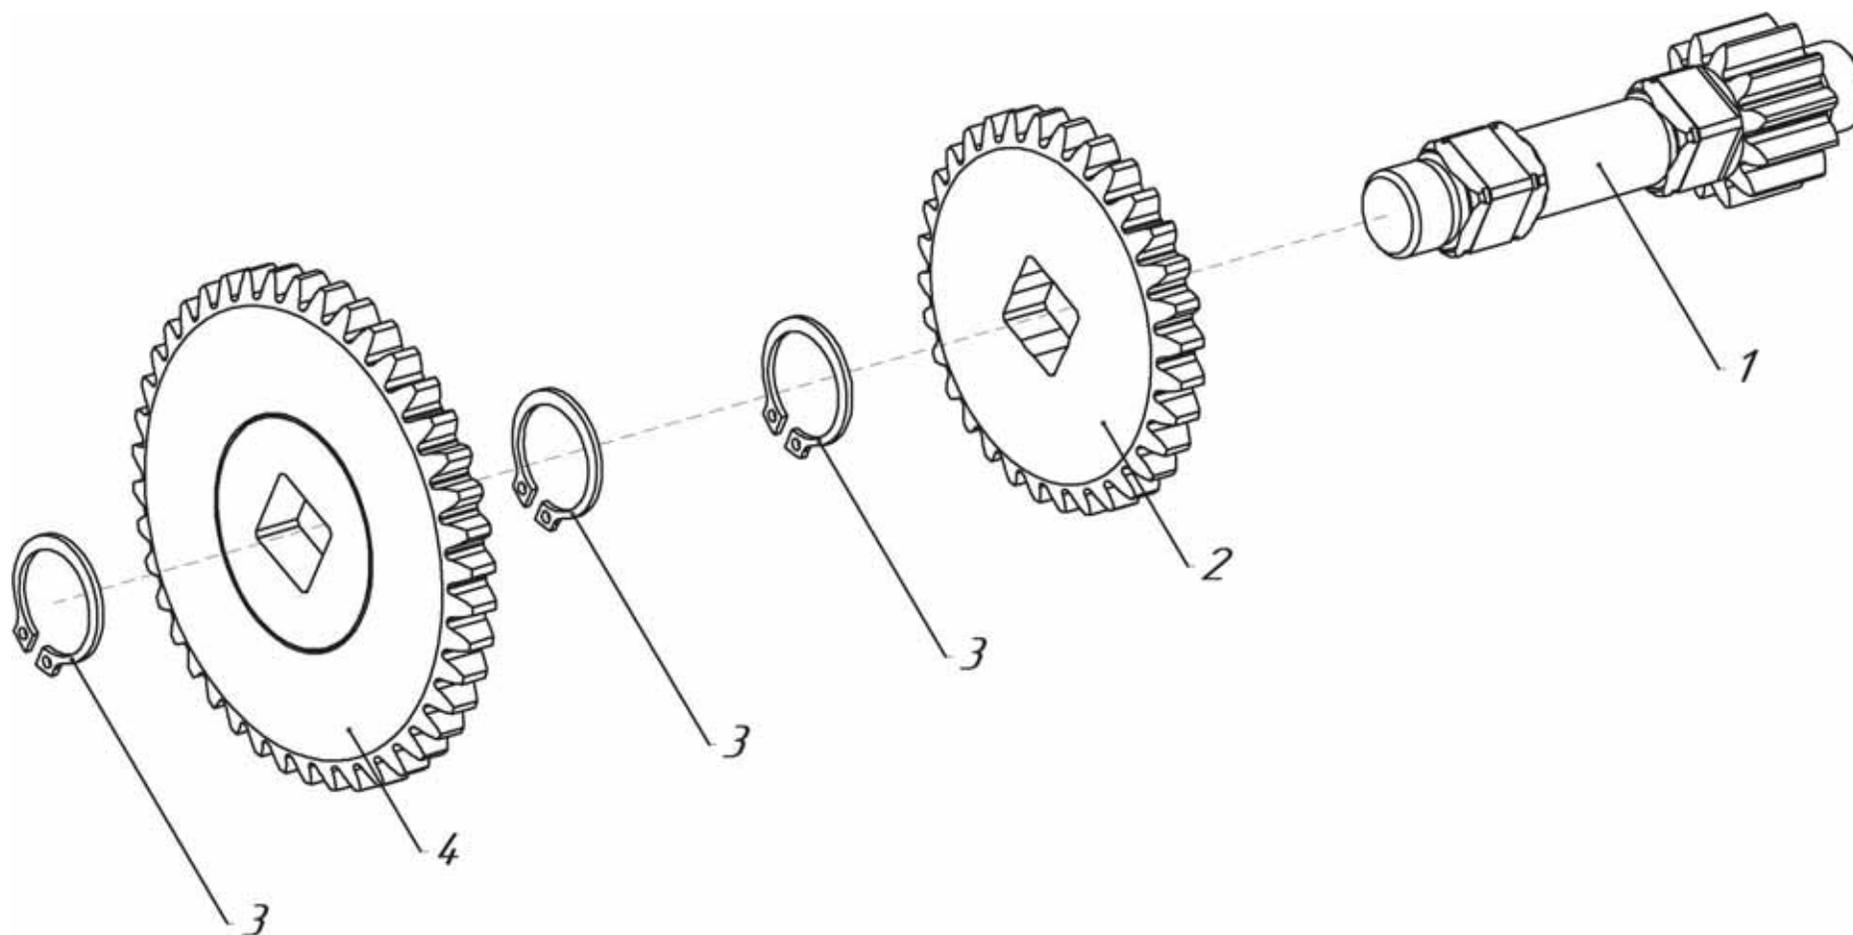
(005.67.0670-01 Вал промежуточный в сборе)
